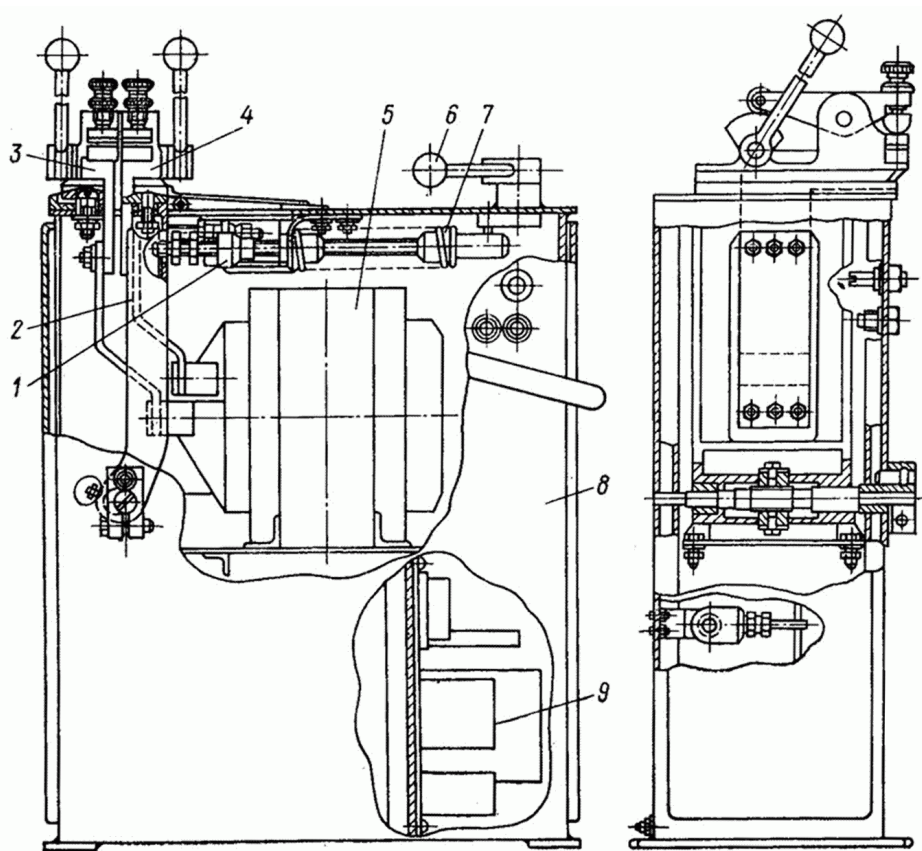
Машина МС-301 для сварки сопротивлением и оплавлением: 1 – регулировочный винт; 2 – рычаг; 3 – неподвижный зажим; 4 – подвижный зажим; 5 – сварочный трансформатор; 6 – рычаг привода осадки; 7 – силовая пружина; 8 – корпус; 9 – блок управления с электромагнитным контактором
